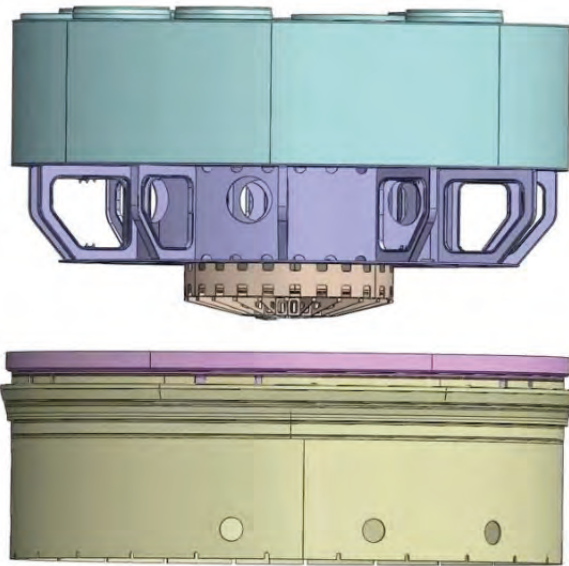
vue du récupérateur de corium, au centre, sous le sommier
